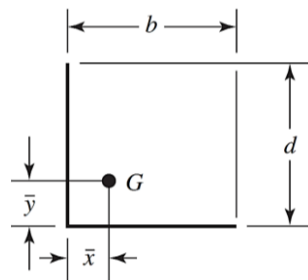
Soldadura filete para ángulo de perfil tipo L [68].
